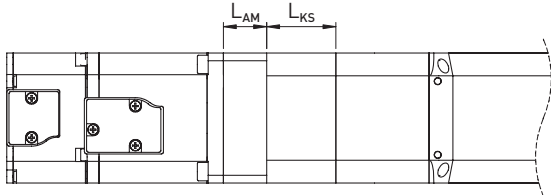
Motoranbindung Linearmodule HM-S ohne Riementrieb
